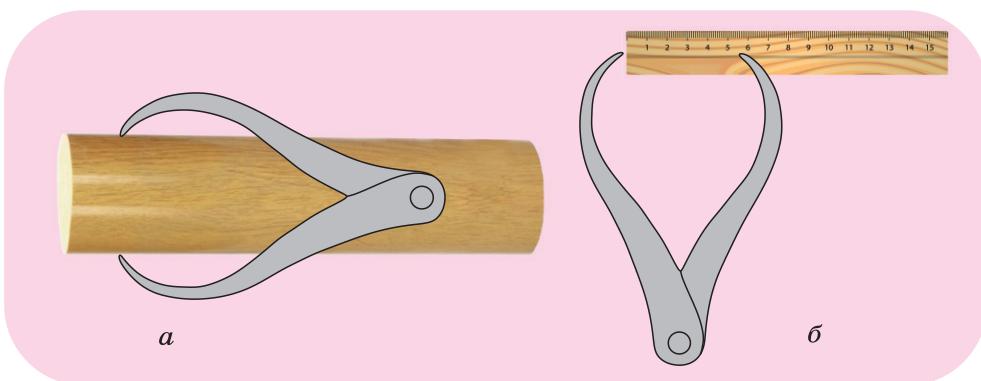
Контроль диаметра круглой детали: а – измерение размера кронциркулем; б – отсчет размера по линейке
